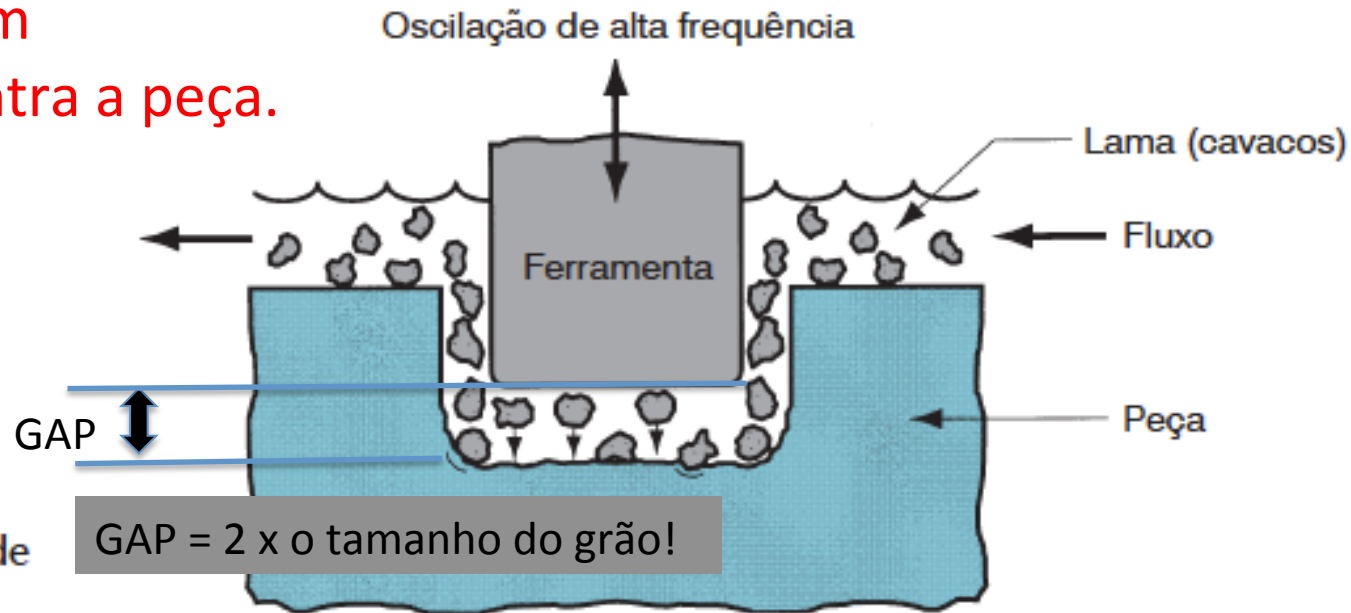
Usinagem por ultrassom. (Crédito: *Fundamentals of Modern Manufacturing*, 4ª Edição, por Mikell P. Groover, 2010. Reimpresso com permissão de John Wiley & Sons, Inc.)
